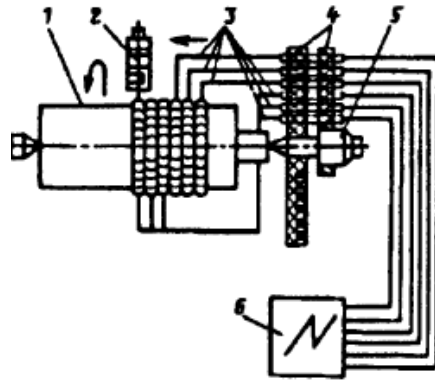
Схема вимірювання температури на поверхні заготовки: 1 – заготовка; 2 – плазмотрон; 3 – термопари; 4 – колектор; 5 – обертовий центр; 6 – осцилограф.
